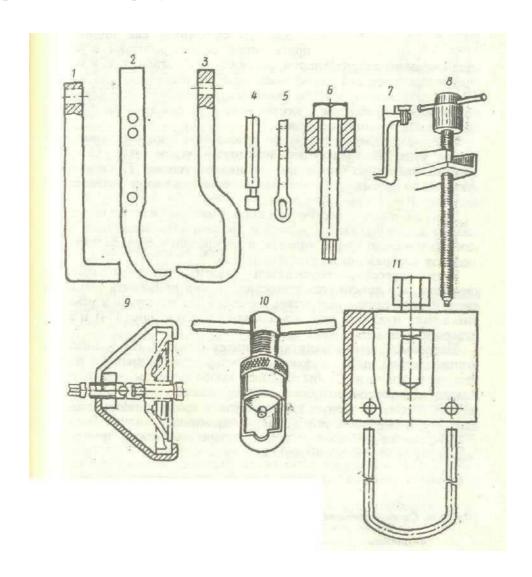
ахваты различной формы: 1, 2, 3 и 7- лапчатые простые; 4- эксцентриковый; 5, 6 и 8- захваты-тяги; 9 и 10- захваты, жестко связанные с корпусом; 11- захват-вилка
